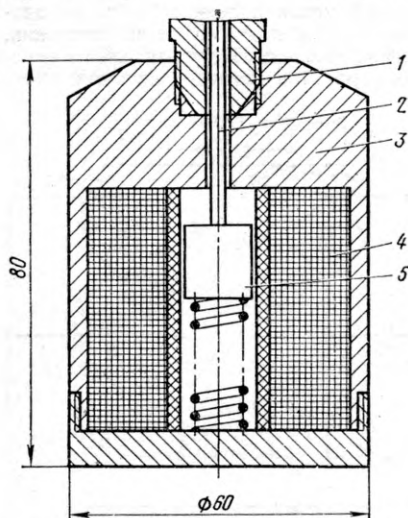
Датчик начала подъема иглы форсунки: 1 — сливной штуцер форсунки; 2 — толкатель; 3 — корпус датчика; 4 — катушка; 5 — постоянный магнит
